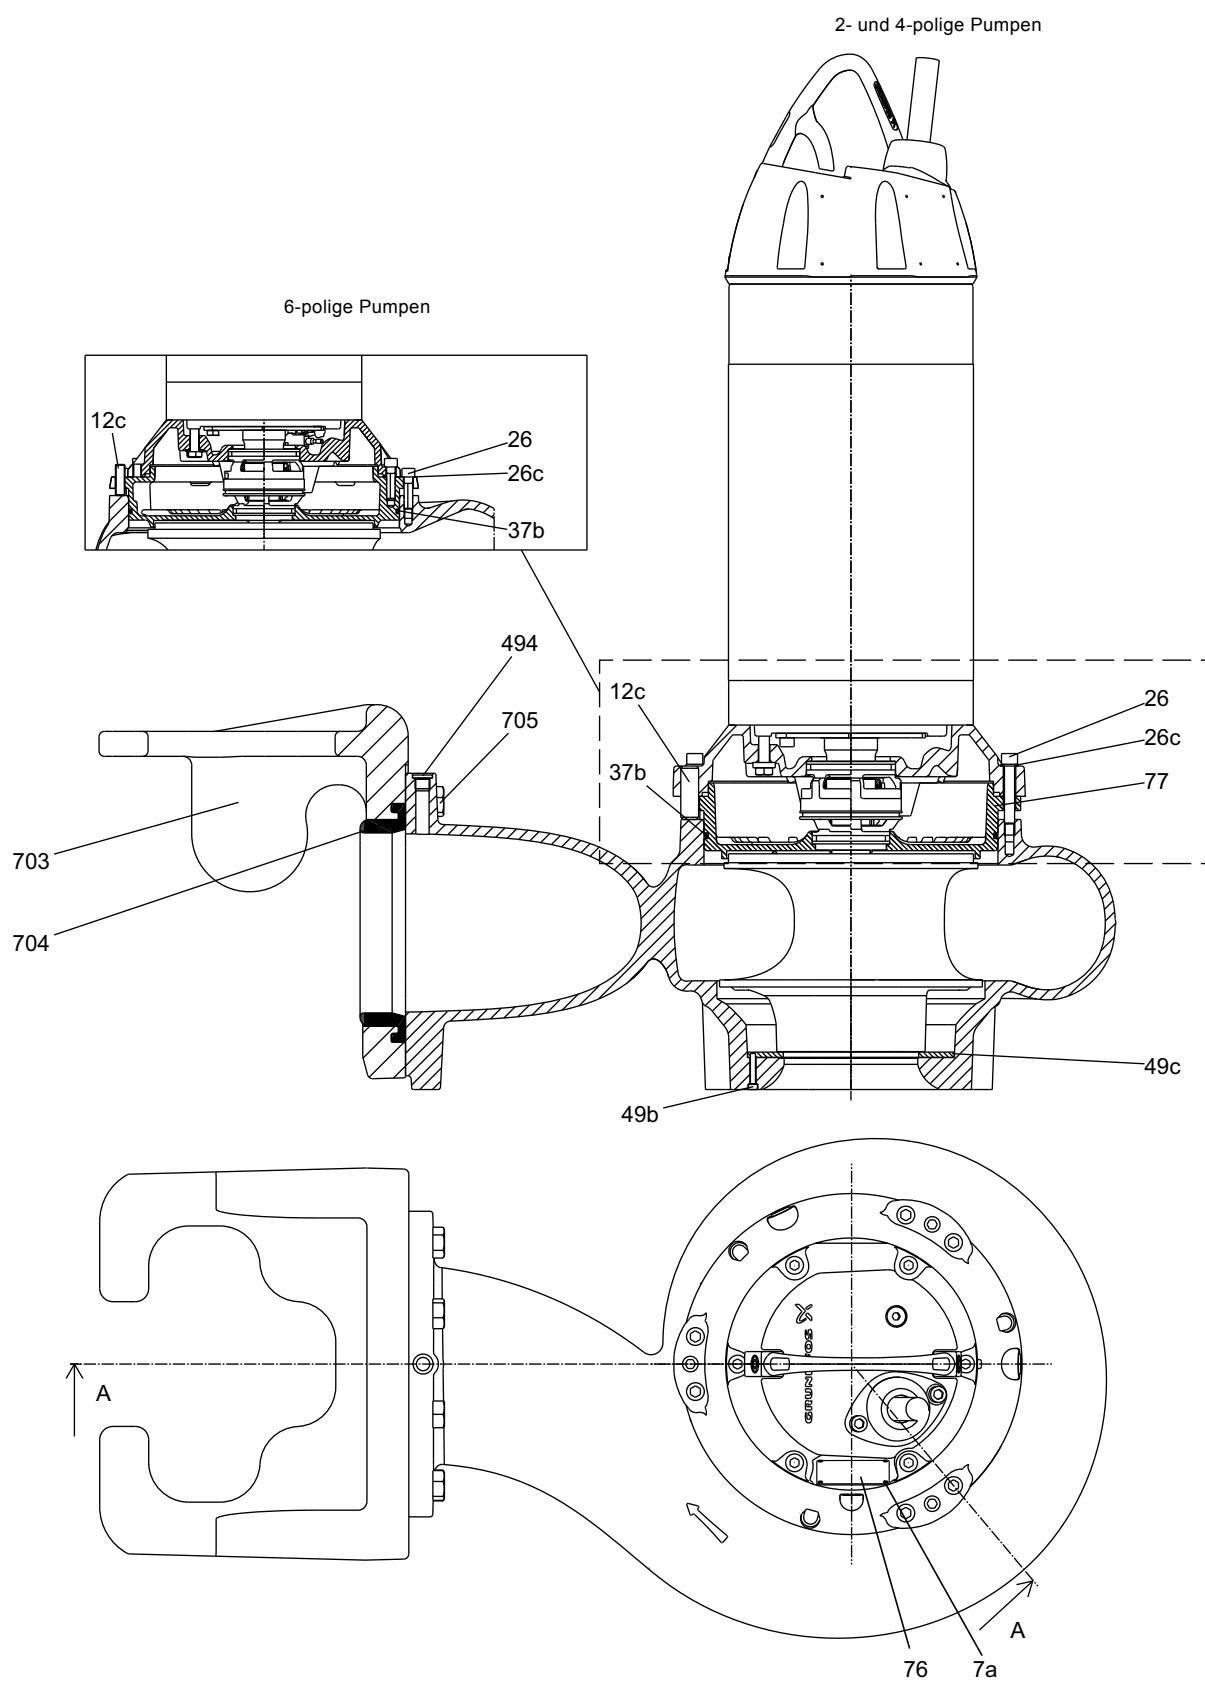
SL-Pumpen ohne Kühlmantel mit 6-poligem Motor
